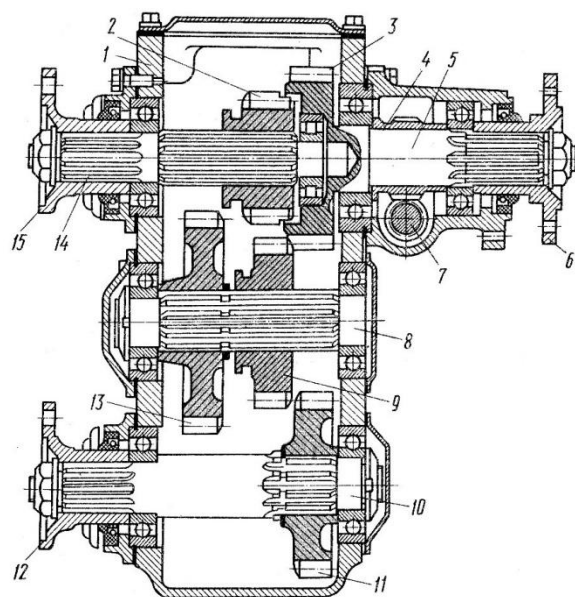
Раздаточная коробка: 1 – картер; 2 – шестерня прямой передачи; 3,9,11,13 – шестерни; 4 – шестерня привода спидометра; 5 – вал привода заднего моста; 6,12,15 – втулки с фланцами; 7 – привод спидометра; 8 – промежуточный вал; 9,13 – шестерни; 10 – вал привода переднего моста; 14 – ведущий вал
